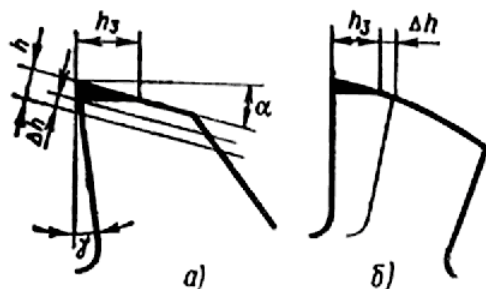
Схемы износа и переточки зуба фрезы:
